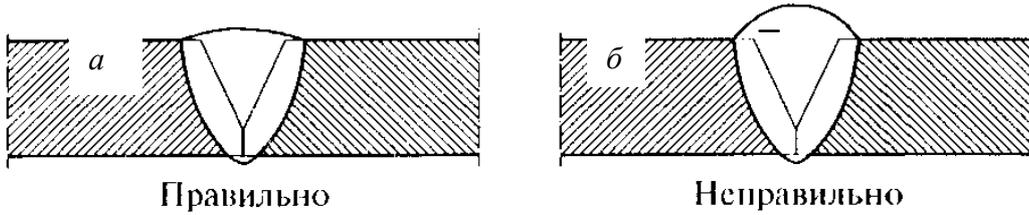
Превышение усиления сварного шва: *a* – нормативный сварной шов; *б* – превышение уровня усиления
